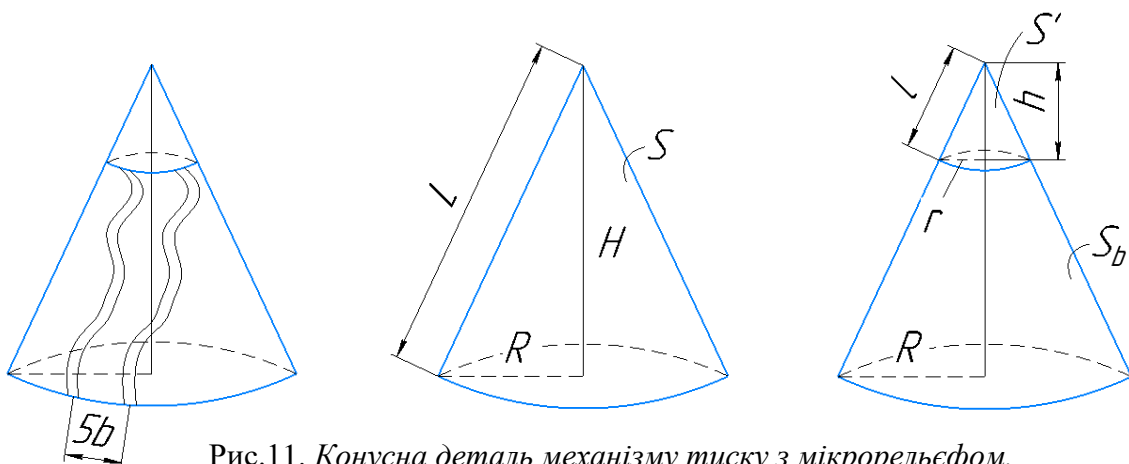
Конусна деталь механізму тиску з мікрорельєфом.
